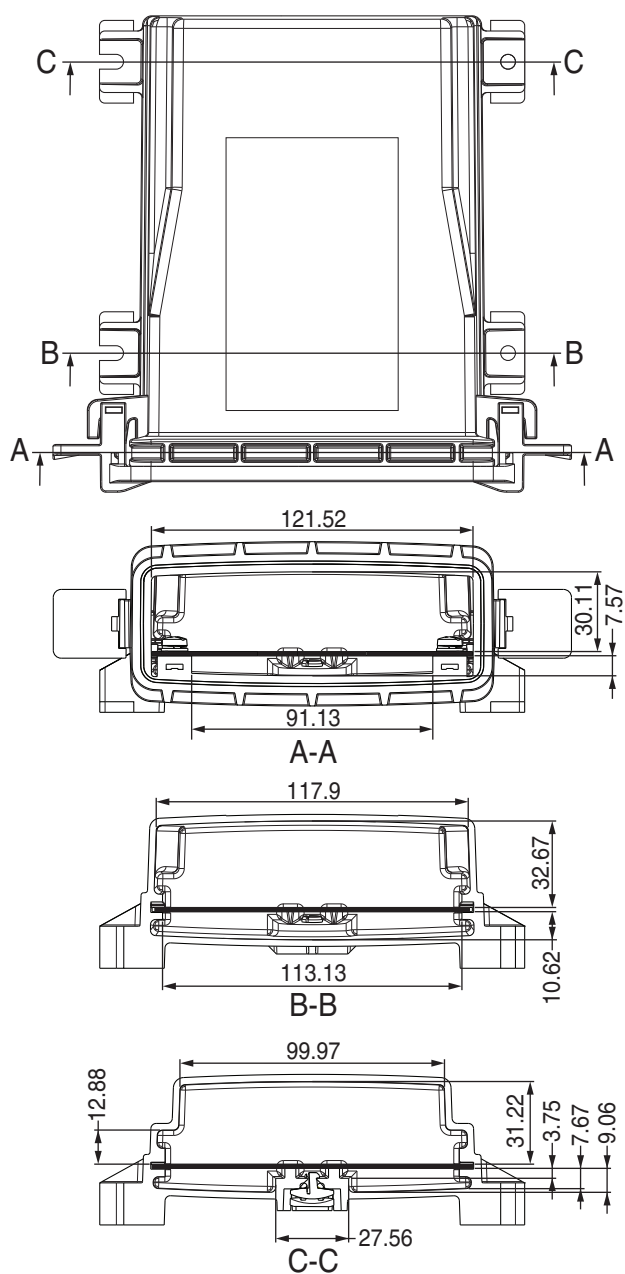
Innenansicht Gehäuse mit Leiterplatte
